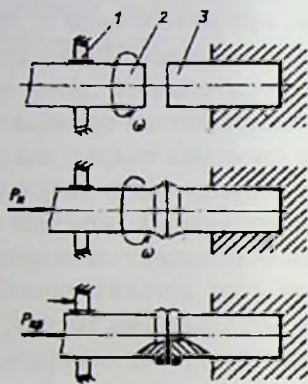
Схема сварки трением с непрерывным приводом:
